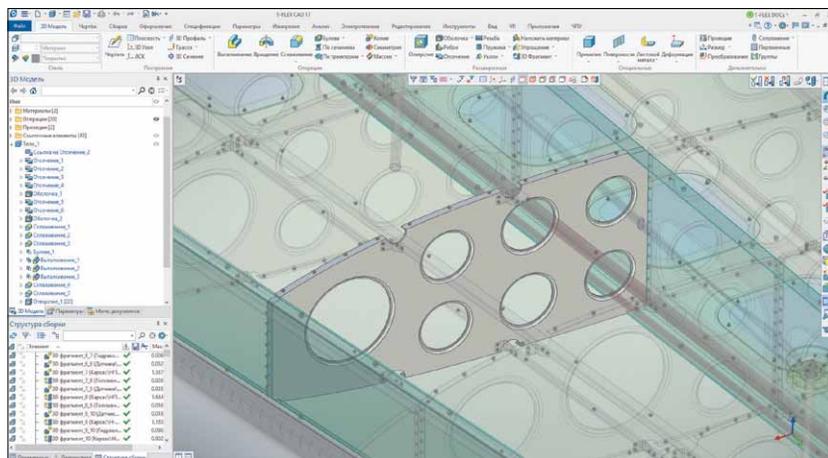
Типовой элемент конструкции крыла в контексте сборки в T-FLEX CAD
